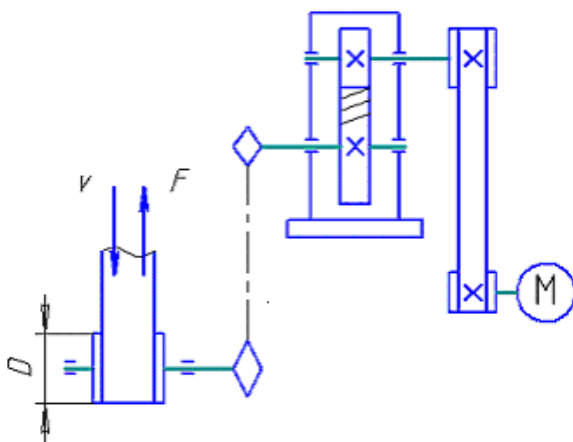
Кинематическая схема привода ленточного конвейера, содержащая одноступенчатый редуктор, ременную и цепную передачи
